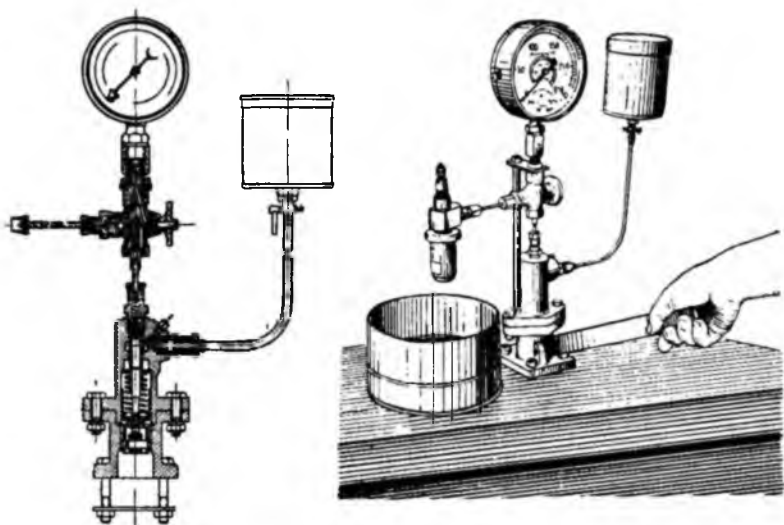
Прибор для регулировки форсунок ККАЗ.
